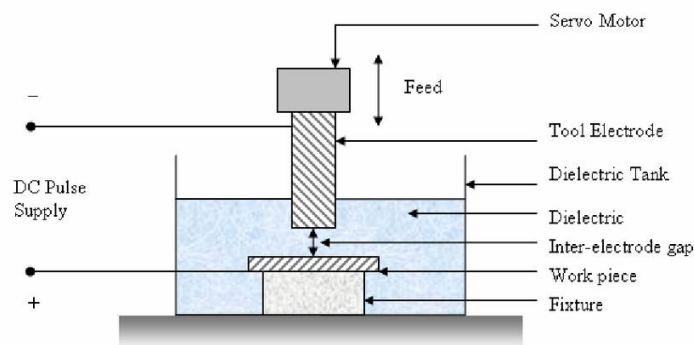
Schéma de principe de l'électroérosion (ou EDM, pour electrical discharge machining) [12].
